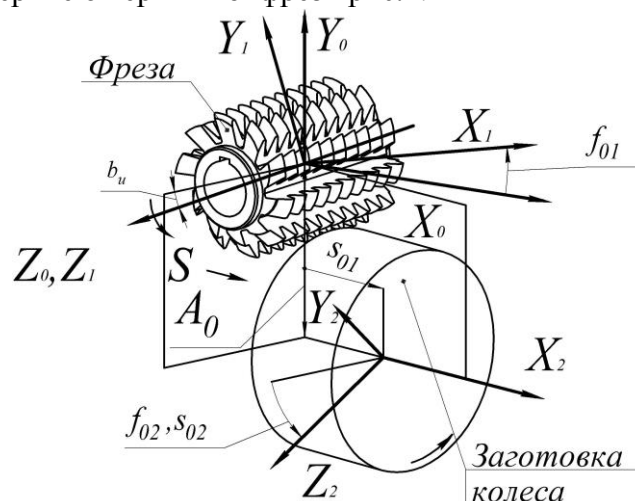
Розрахункова схема формоутворення косозубих зубчастих коліс черв'ячними фрезами.
